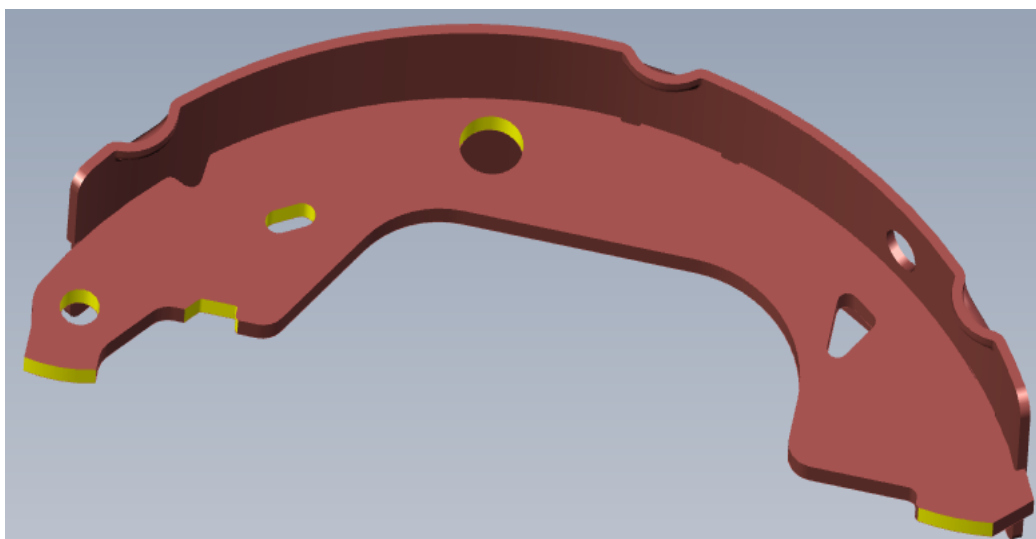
Imagem de um segmento estampado após soldadura e calibração.
